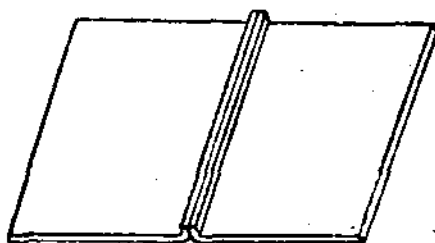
Листы алюминия с загнутыми для сварки кромками.
